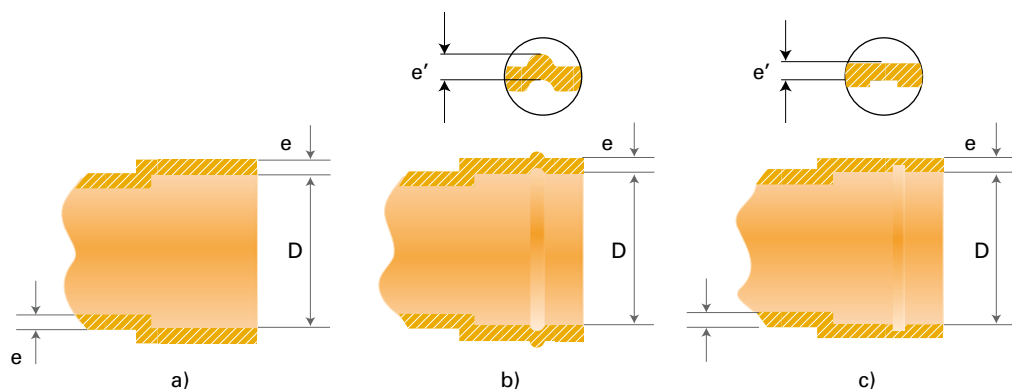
Accesorio con anillo de soldadura incorporado. Espesor mínimo
